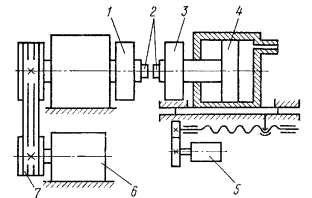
Принципиальная кинематическая схема машины для сварки трением:
